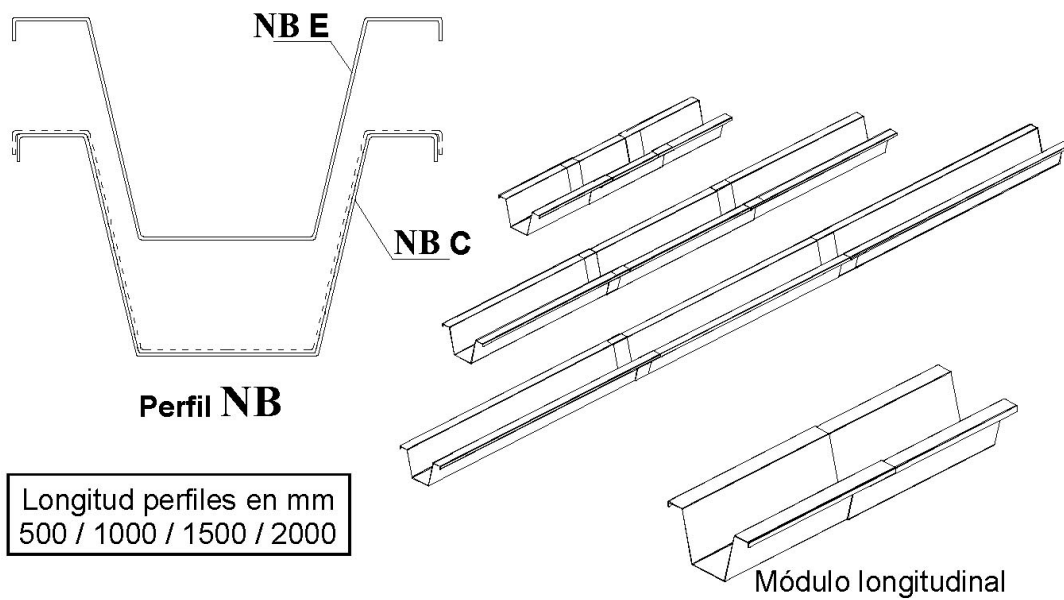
PERFILES UNIDOS POR SOLDADURA.
